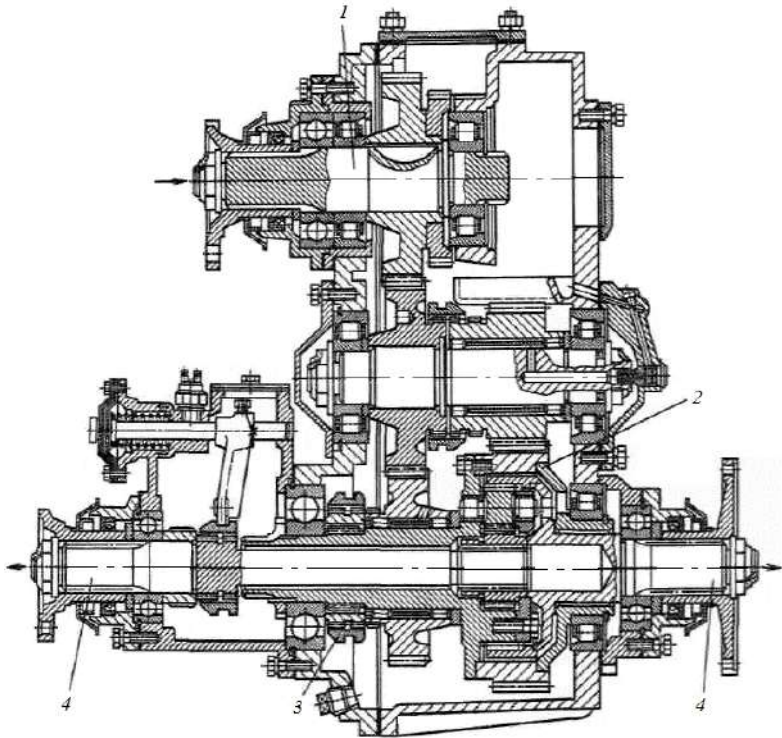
Роздавальна коробка КамАЗ-4310: 1 – ведучий вал; 2 – несиметричний диференціал; 3 – блокуюча муфта; 4 – ведені вали
